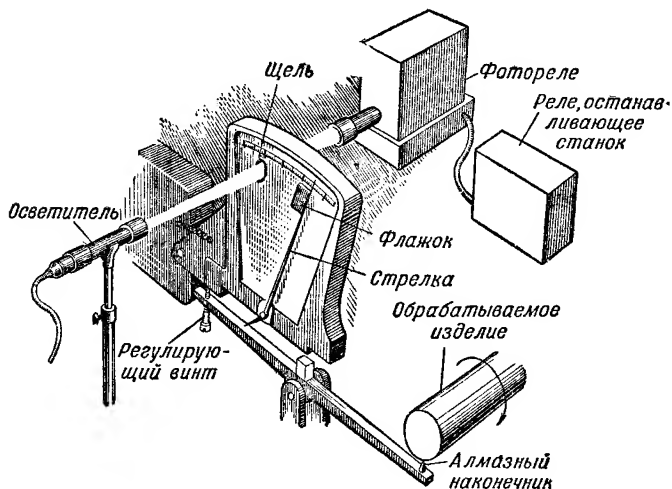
Устройство для контроля толщины обрабатываемого изделия
